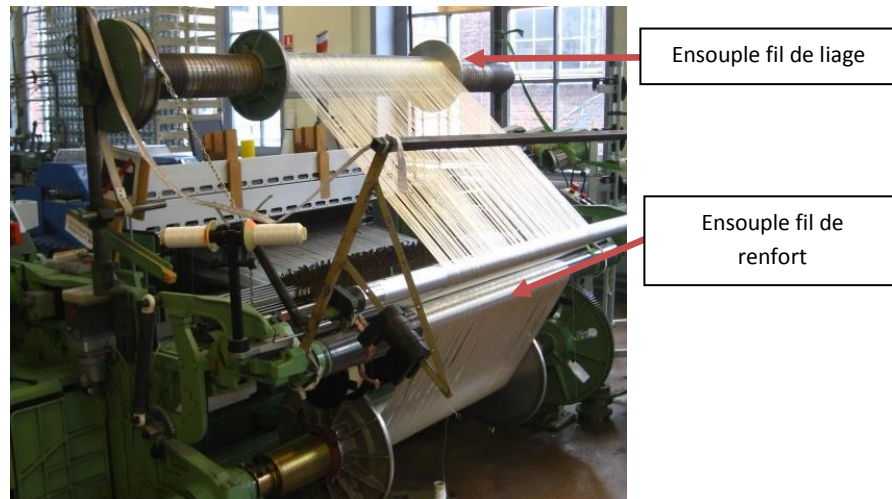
Modification machine à tisser pour le tissage interlock.
